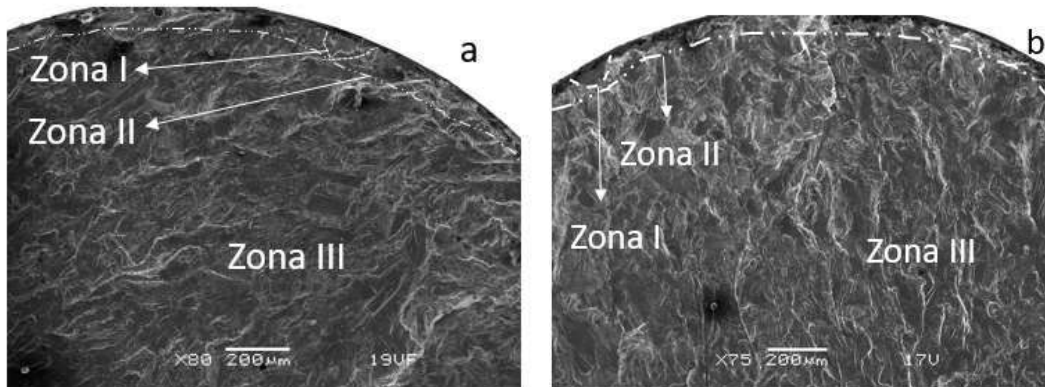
a). Fractografía de las diferentes zonas de la superficie de fractura del I-718 a 746 MPa y b), Fractografía de las diferentes zonas de la superficie de fractura del I-718 a 667 MPa.
